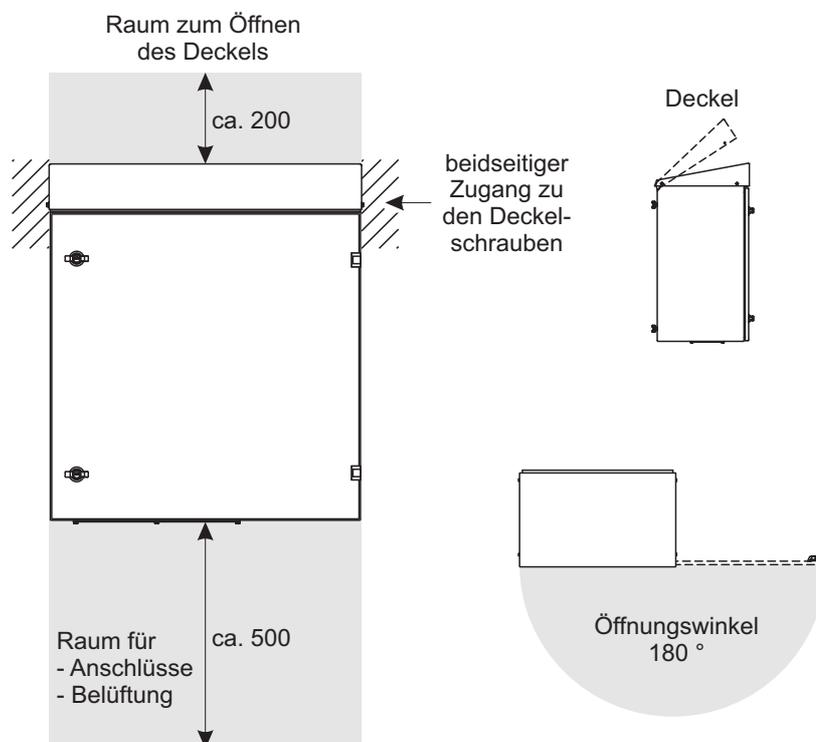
Maßzeichnung Alyza IQ Gehäuse (Maße in mm)
